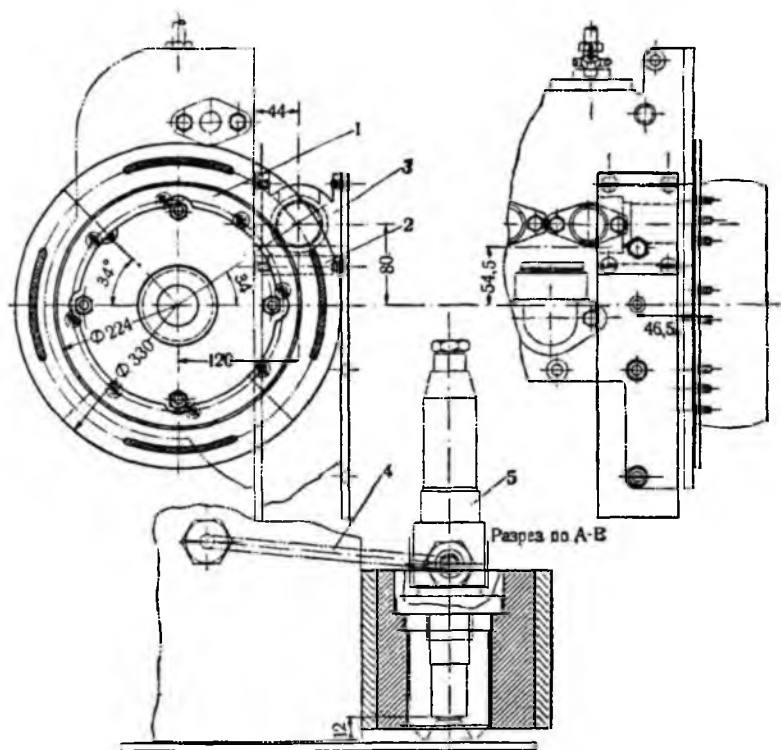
Монтаж приспособления для механического контроля вырыска топлива.
